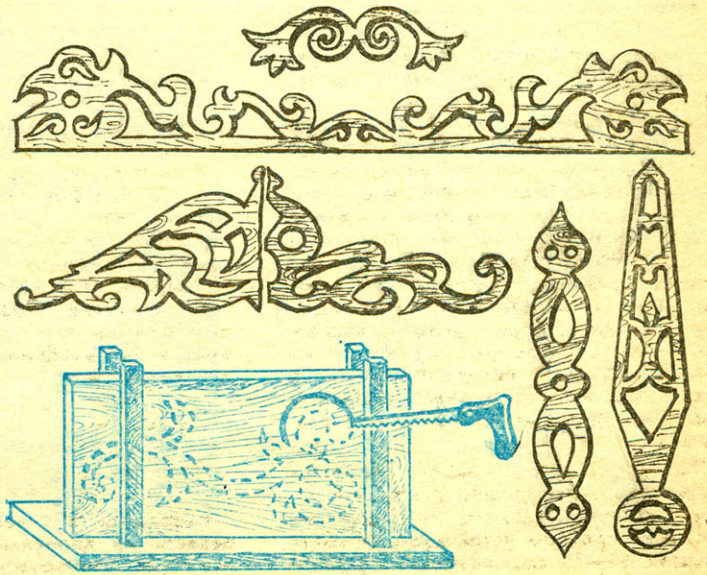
Прорезная резьба и приспособление для ее выполнения.
